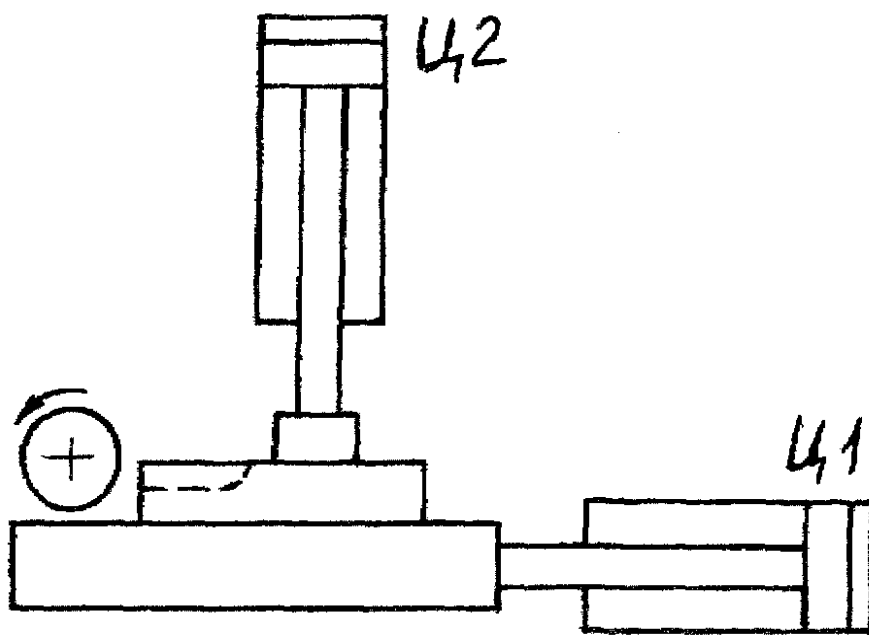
Конструктивная схема подачи стола фрезерного станка
